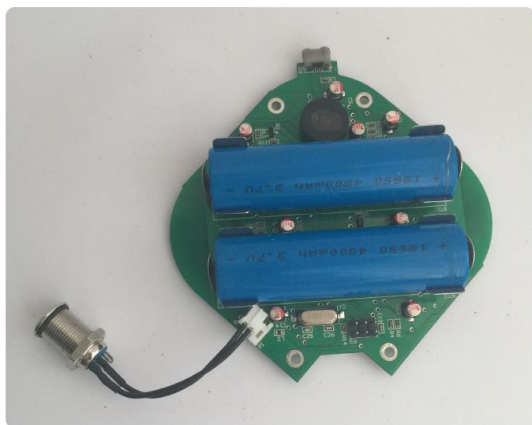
Imagen de las pilas recargables y de larga duración entregadas por Cratus.
